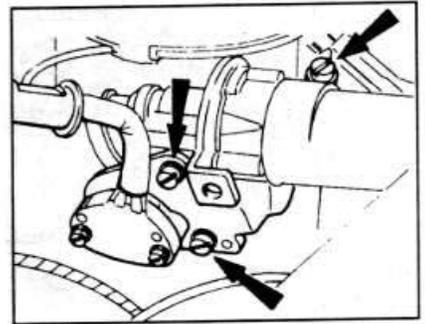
В.18. Расположение винтов крепления подвески двигателя управления дросселем.
